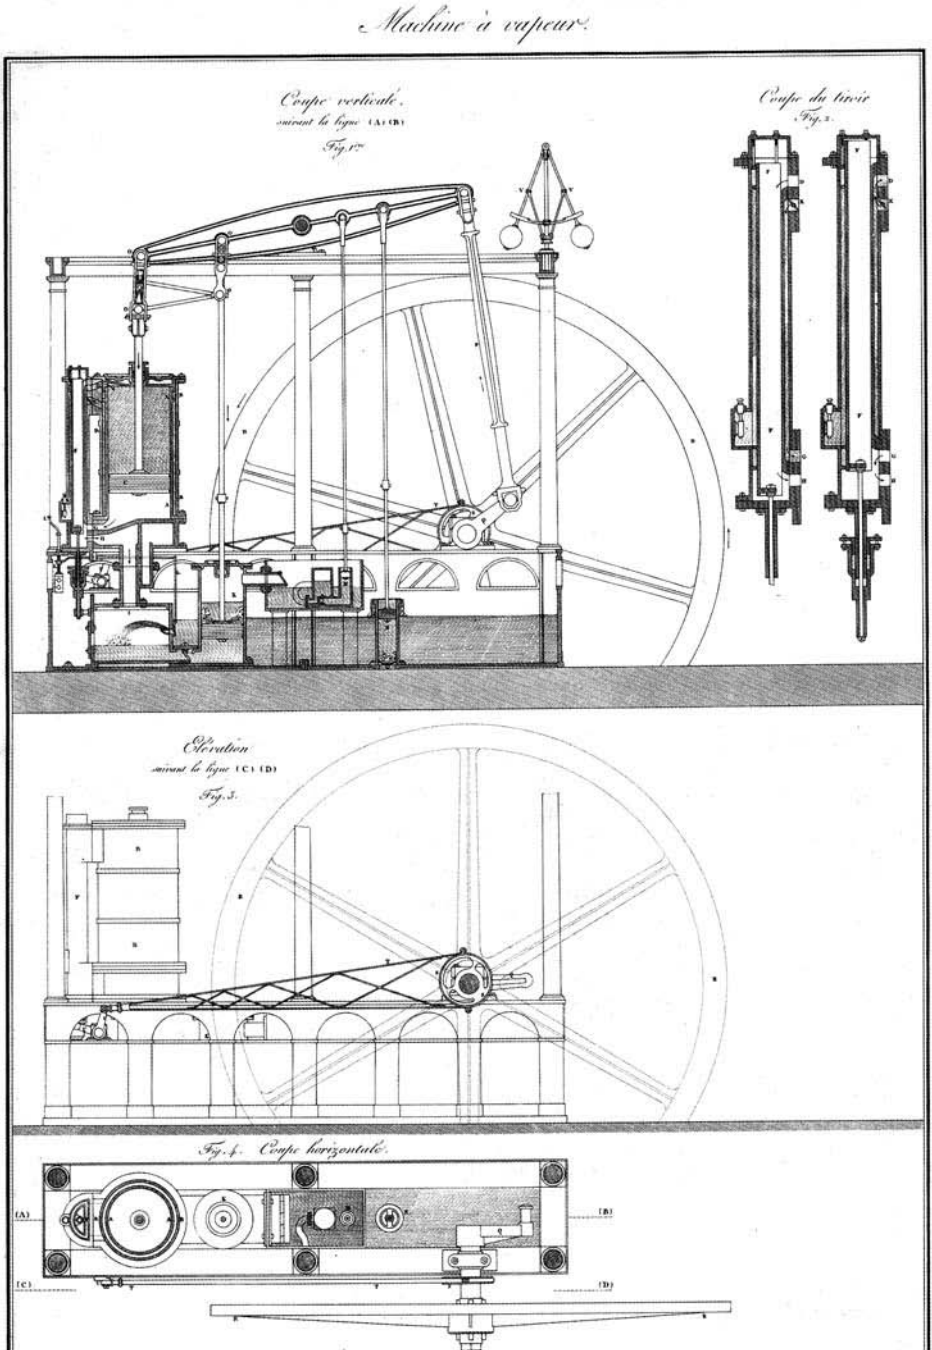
Dessin d'une machine à vapeur de Watt, pour le cours de machines d'Arago à l'École polytechnique.
